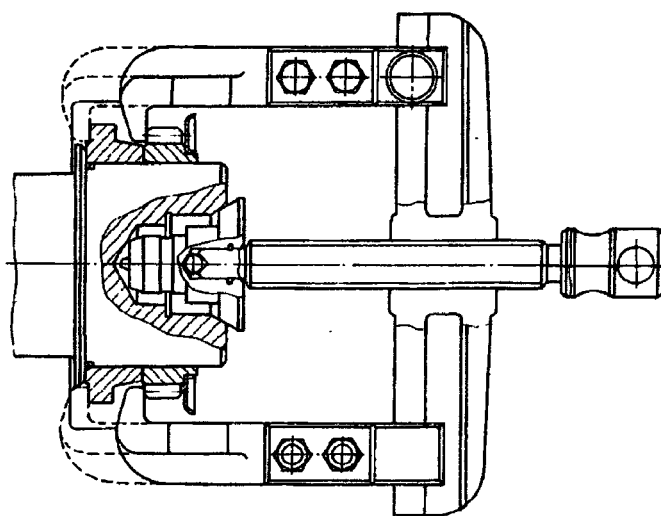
Съемник шестерен и противовесов коленчатого вала из комплекта Н801-02
